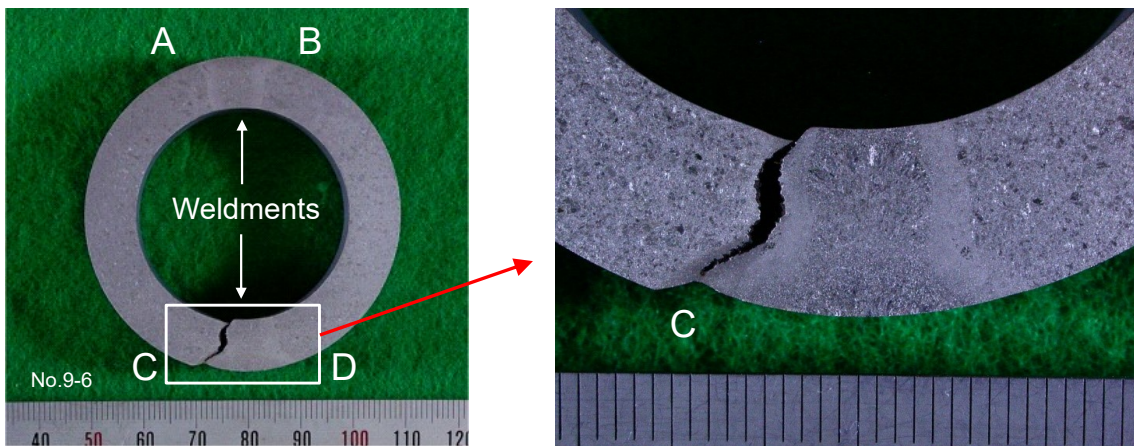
内圧クリープ試験体の破壊後の断面状況(試験体 No. 9-6)
